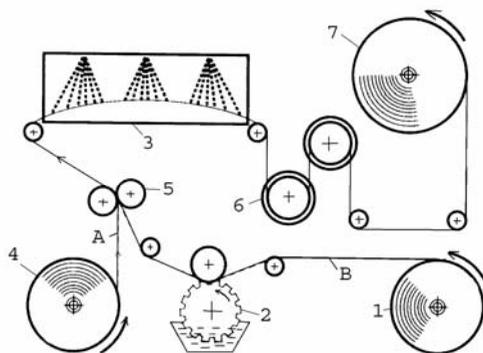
Схема устройства для «мокрой» припрессовки: 1 — размотка материала A; 2 — нанесение покрытия гравированным валом; 3 — сушка; 4 — размотка материала B; 5 — секция ламинирования; 6 — охлаждающие барабаны; 7 — намотка готового ламината
